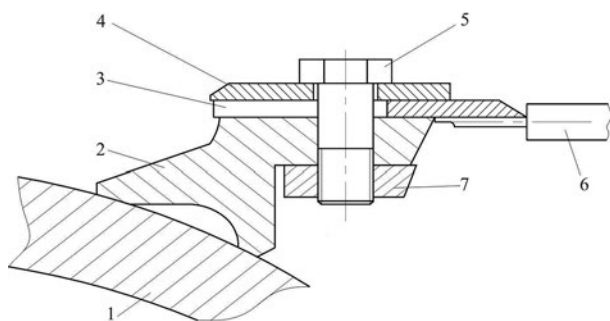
Схема измерения ширины ножа от режущей кромки до опоры барабана: 1 — барабан; 2 — опора; 3 — нож; 4 — прижим; 5 — болт; 6 — штангенциркуль; 7 — пластина
